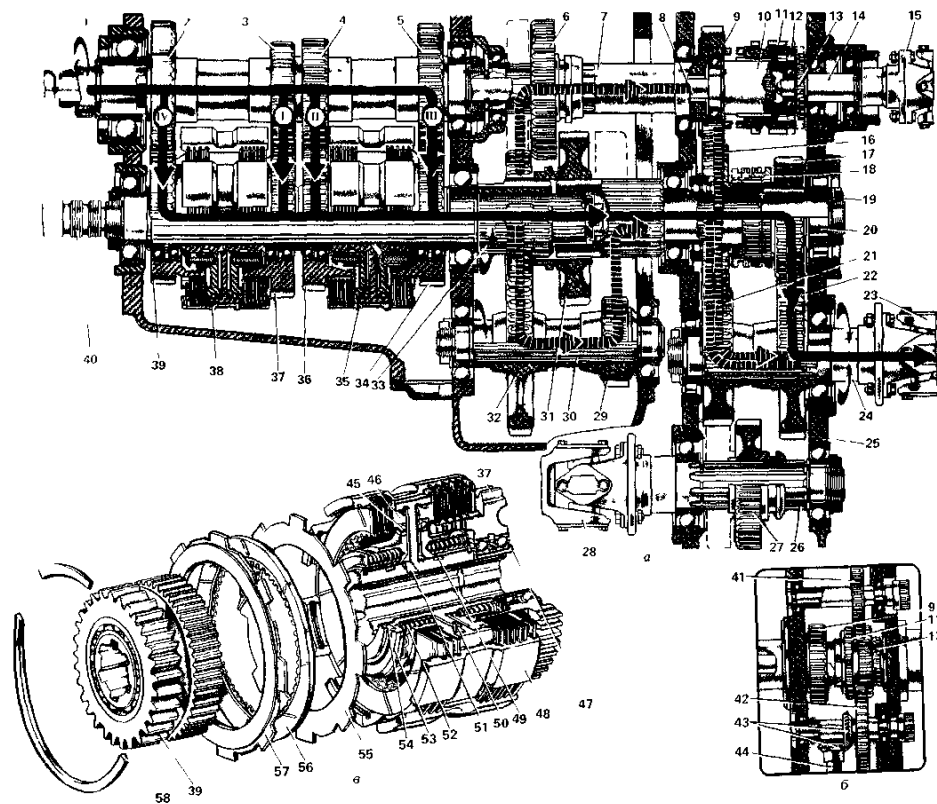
Коробка передач и раздаточная коробка трактора Т-150К:
